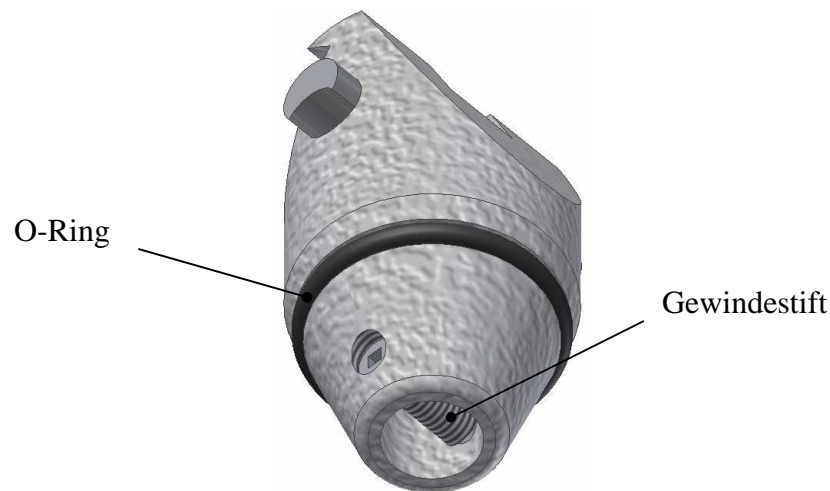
Gewindestift und O-Ring am Verschlusskegel
